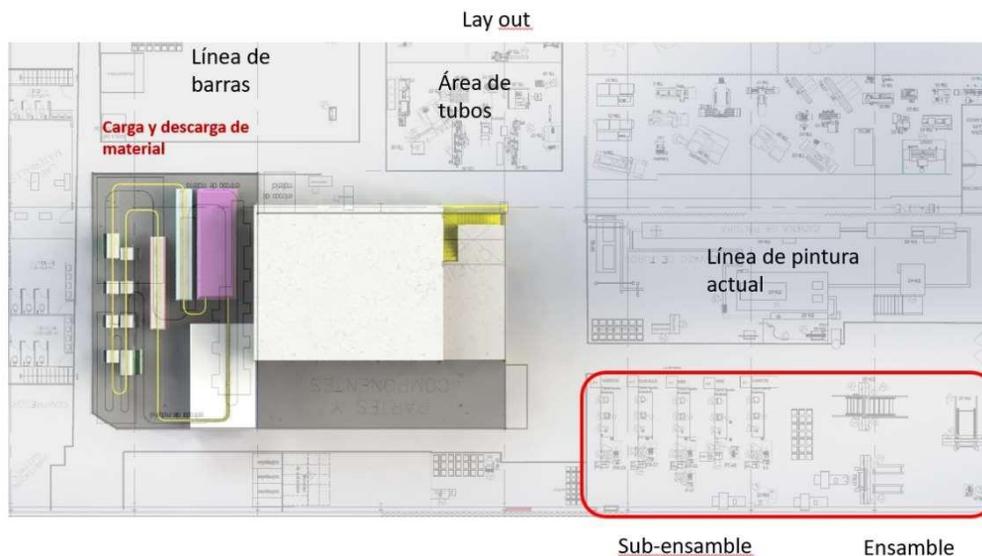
S. Definición de nueva área en layout de la planta (Fuente: Urresko)
